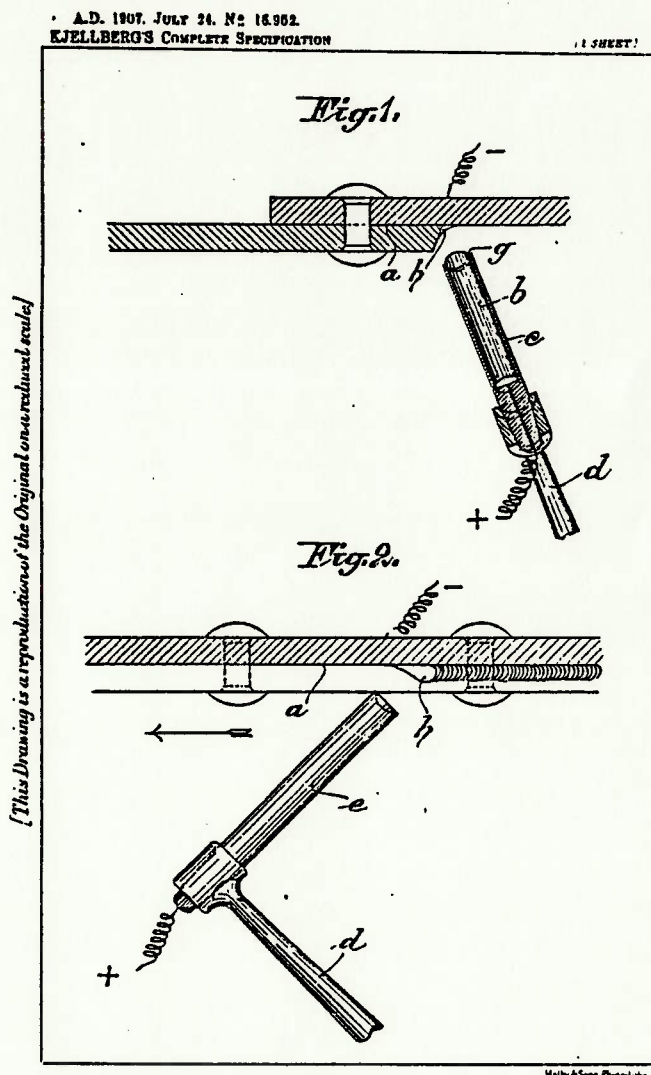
Especificação do processo de soldagem com eletrodo revestido segundo a patente de Kjellberg [47].
